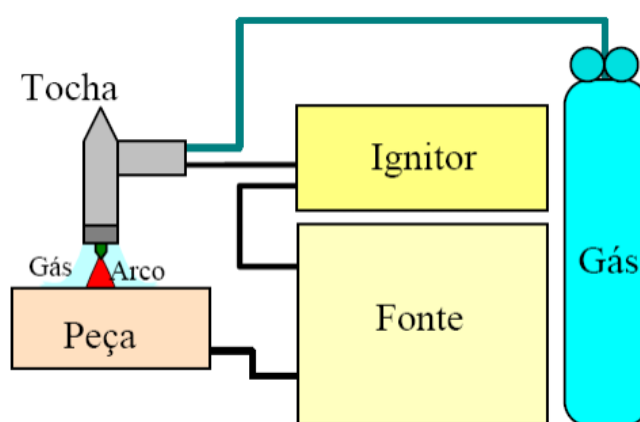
Equipamento para soldagem TIG [Marques et al., 2009]
